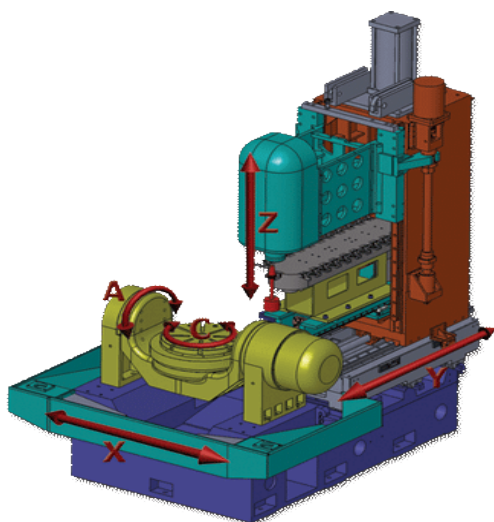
Расположение координатных осей вертикально - обрабатывающего центра 500VS
